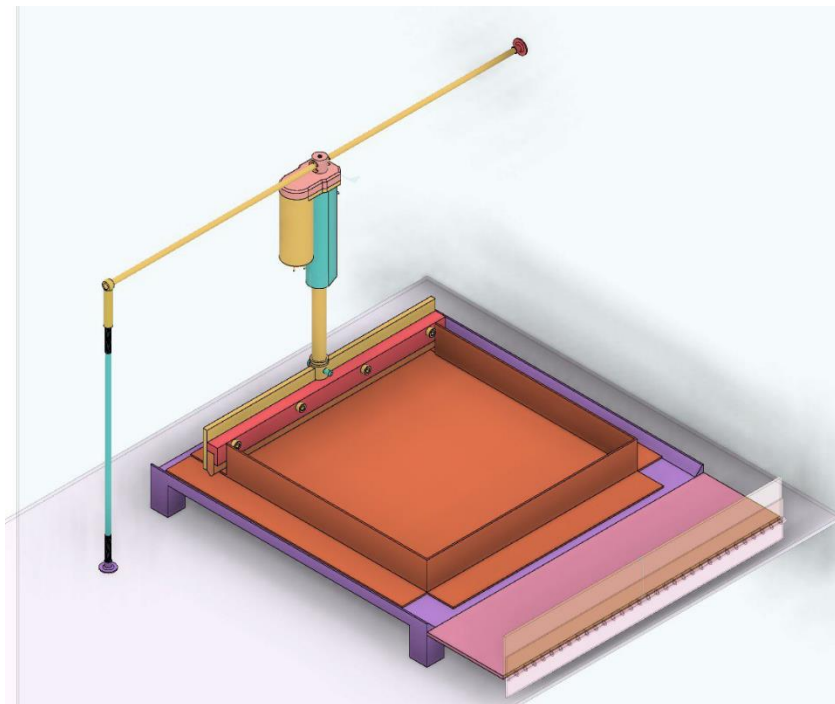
Mecanismo de tope para contener la pizza o la caja.
